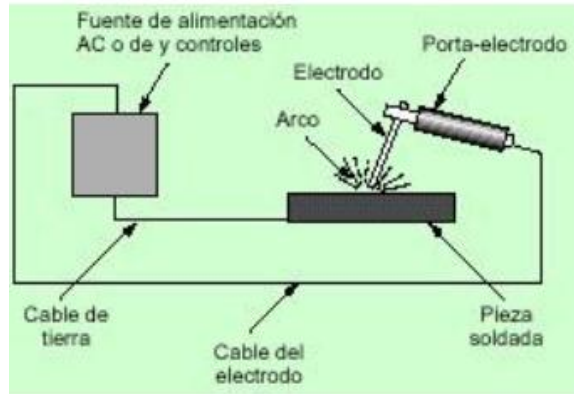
Proceso de soldadura por arco eléctrico
